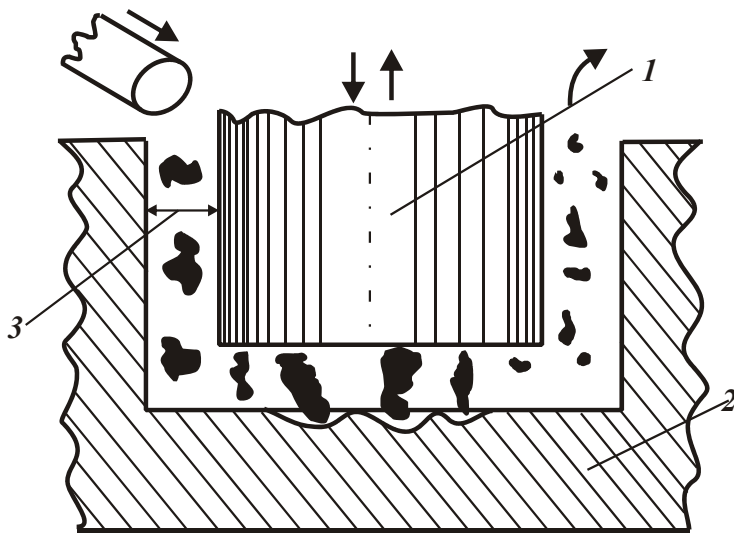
Принципиальная схема ультразвуковой обработки: 1 – вибрирующий инструмент; 2 – обрабатываемое изделие; 3 – зазор между инструментом и изделием, куда вводится абразивная суспензия.
